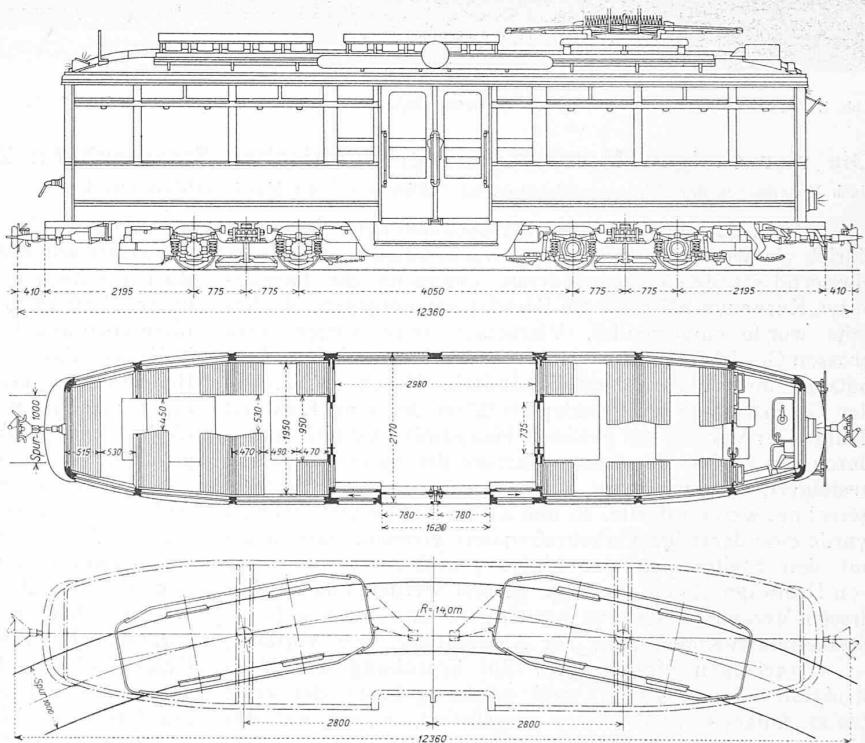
Ansicht und Grundriss des Motorwagens. — Maßstab 1:100.
